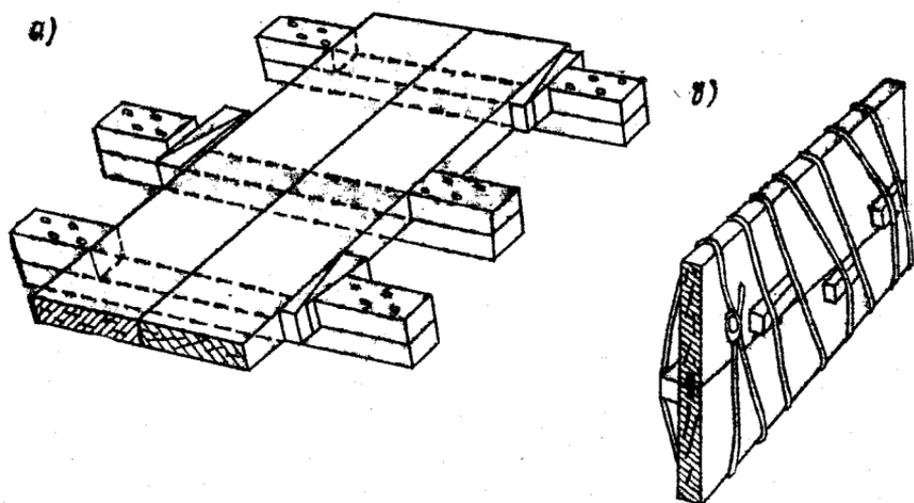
Склейвание щита из досок: а — запрессовка при помощи клиньев в приспособлении; б — при помощи шнура и клиньев.
